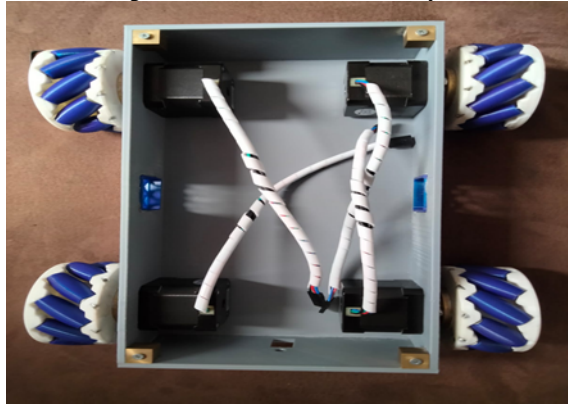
Paso 14. Ya terminado de colocar todas las ruedas con la llave allen, ahora toca armar la tapa de la caja. Sección A y B.
